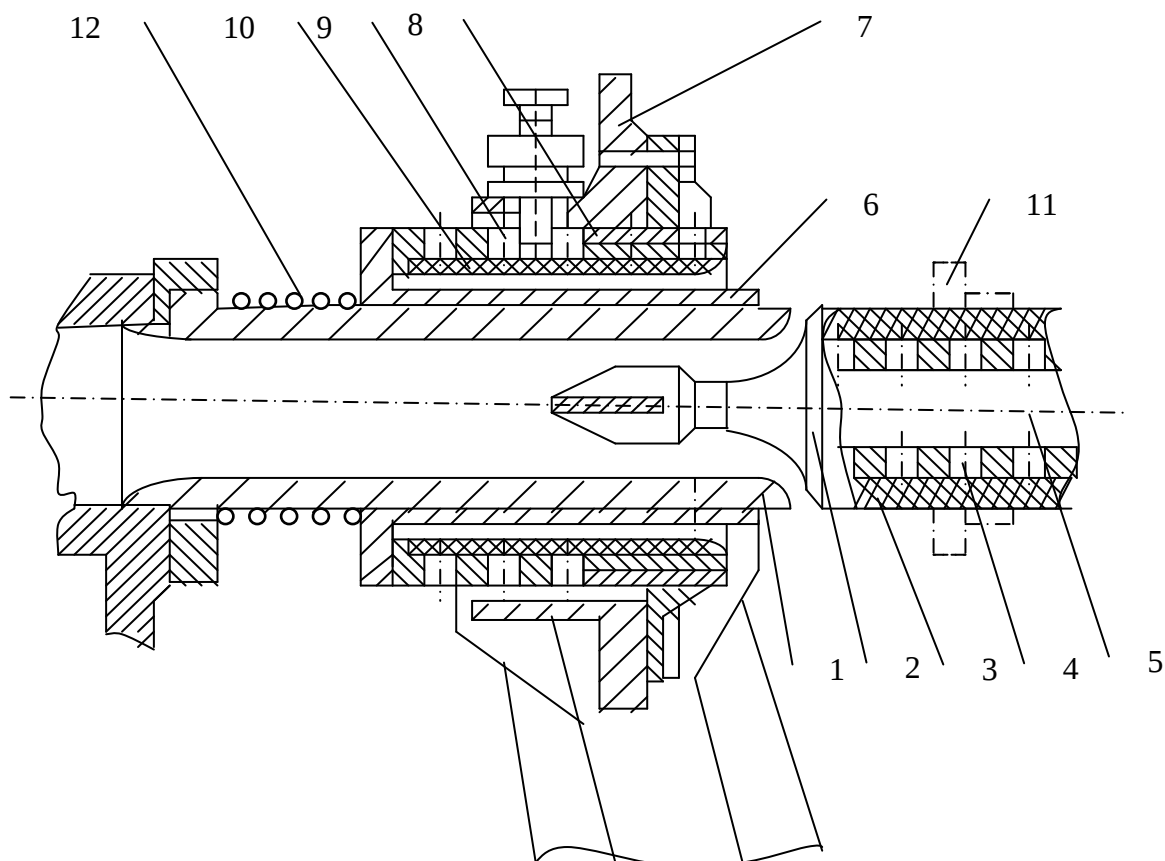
Формующий инструмент для формирования изделий в форме тора
